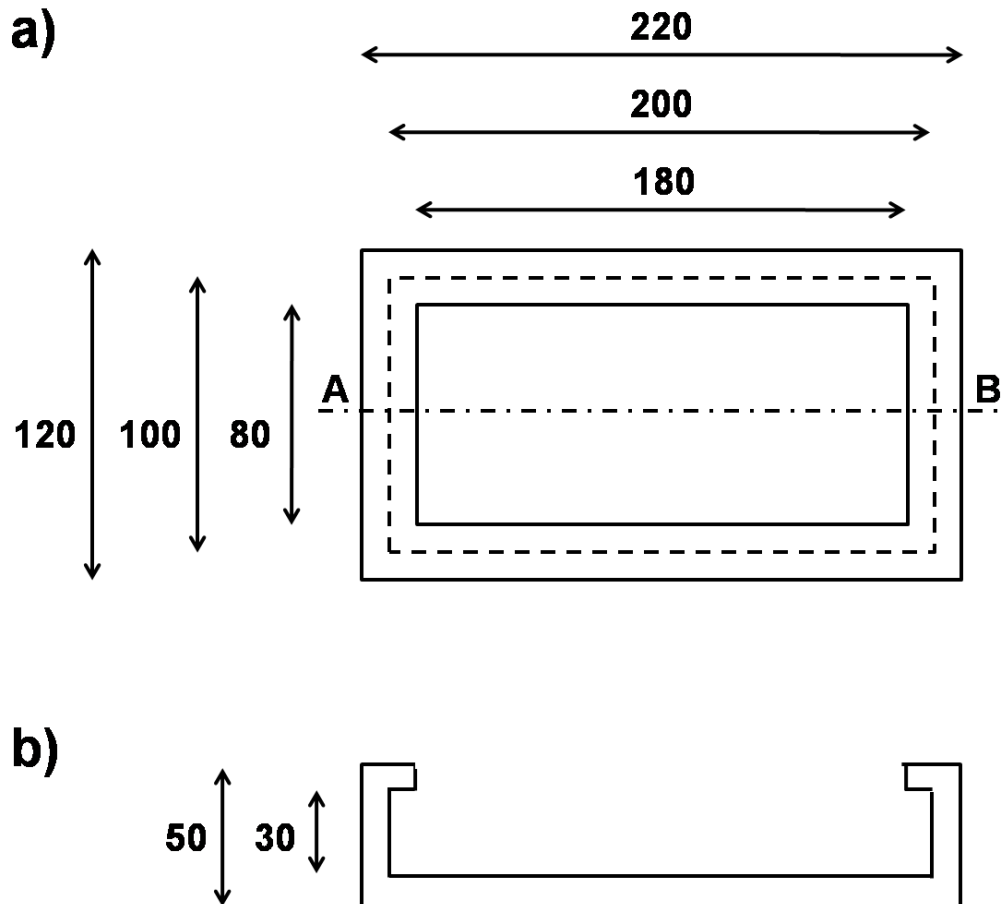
Geometría y dimensiones del IT-B (mm): a) Vista superior, b) Vista frontal.
